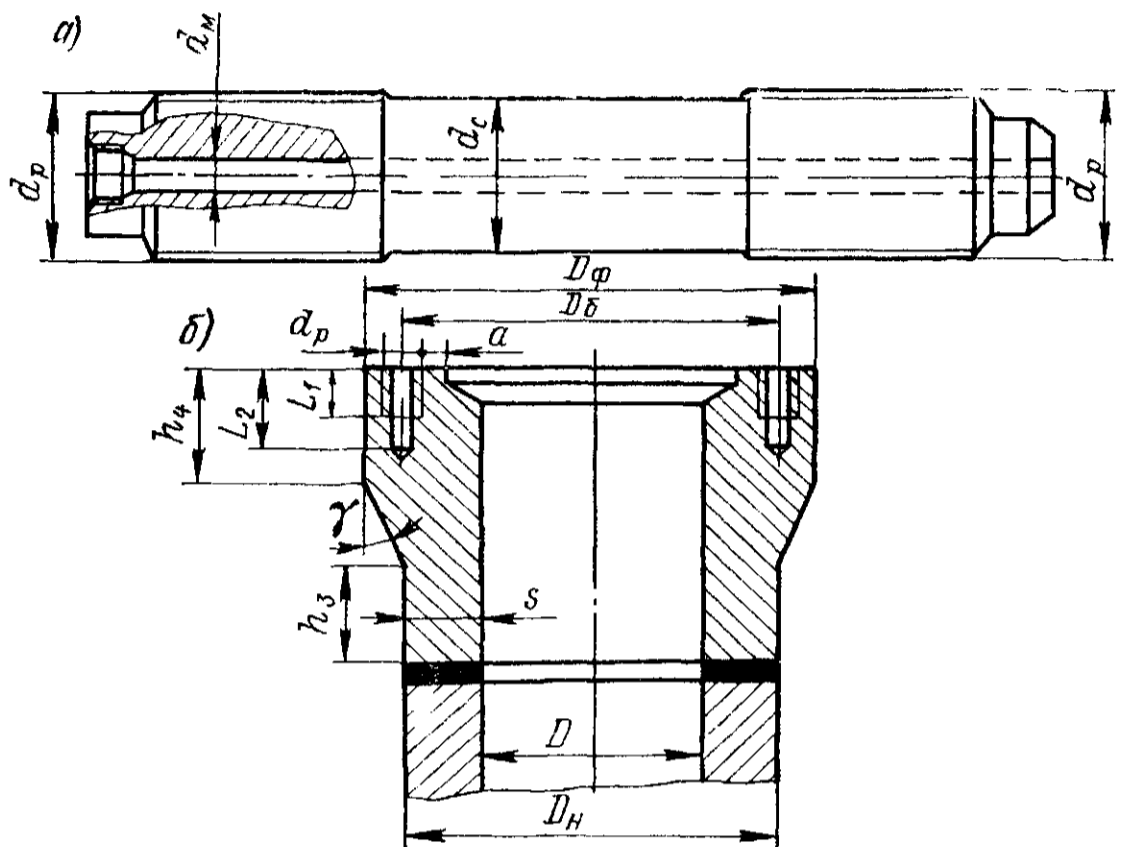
Элементы затворов: а — шпилька; б — фланец
